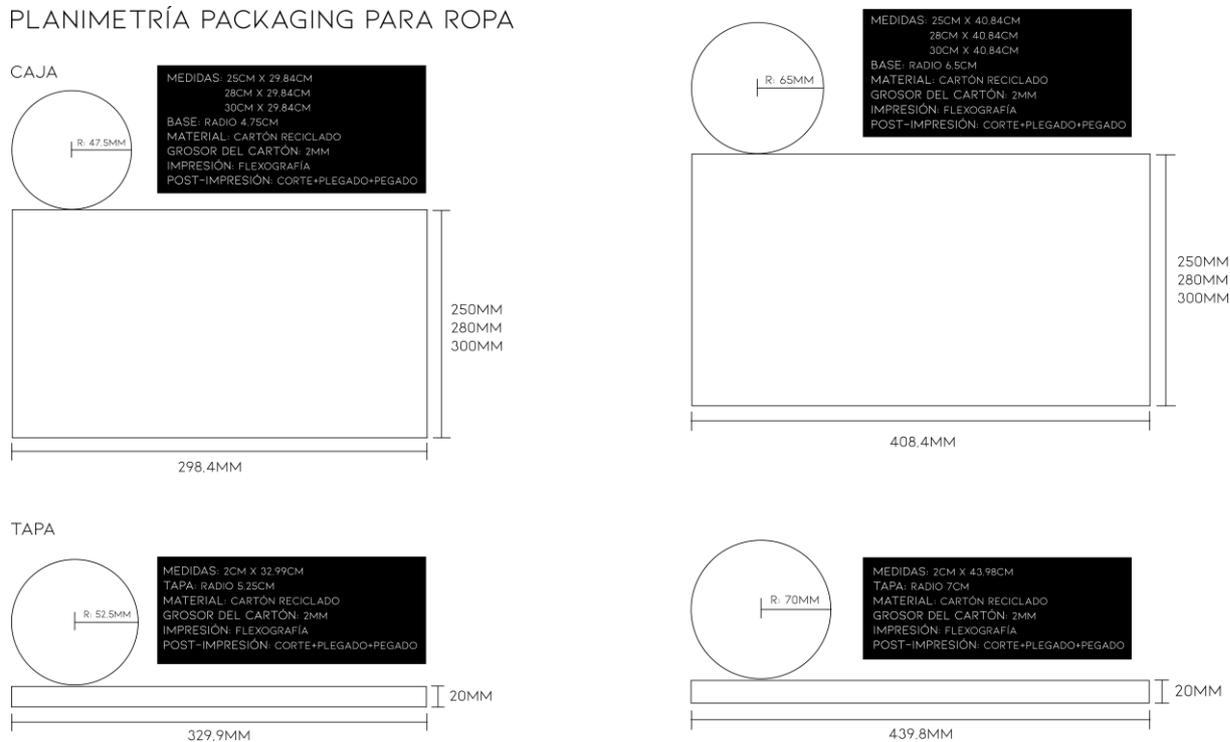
Planimetría packaging para ropa. Fuente: elaboración propia, 2020.
